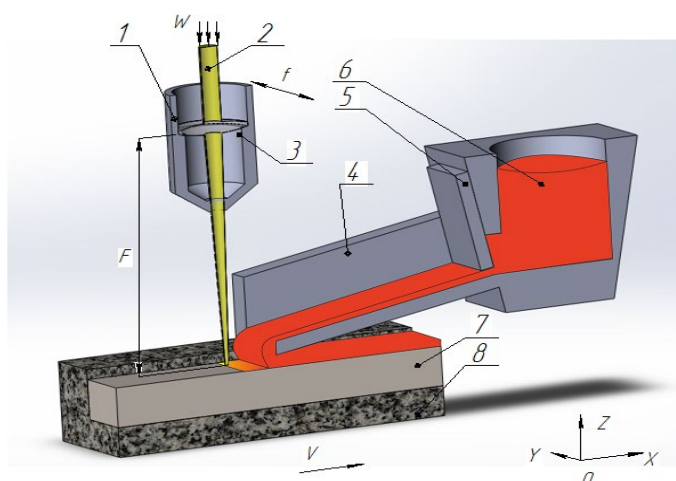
Схема лазерного біметалічного композиту з використанням скануючого лазерного ручка: 1 – сопло; 2 – лазерний пучок; 3 – лінза; 4 – літник; 5 – заслінка; 6 – розплав; 7 – основа; 8 – форма
